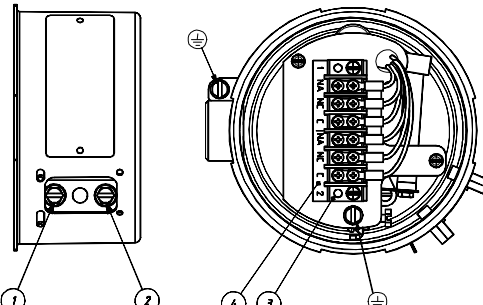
Elektrische Anschlüsse und Einstellschrauben
